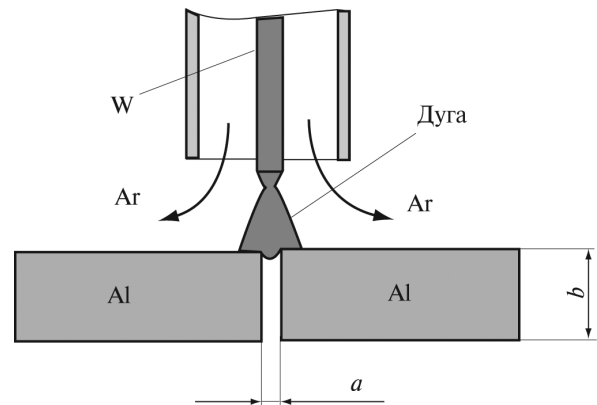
Схема стыкового соединения, собранного под сварку:
